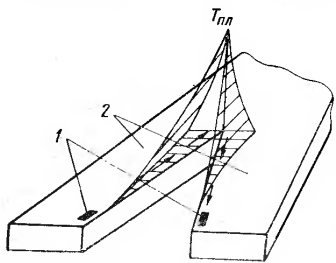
Схема процесса сварки давлением с оплавлением:
